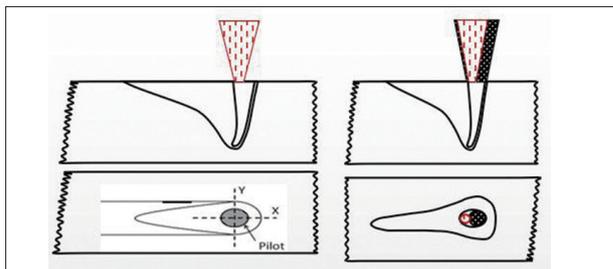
KeyholeFinder 的精细调整包括焊接过程中根据导孔位置进行交叉扫描、实现匙孔检测的重复精度，以及首次焊接时执行
